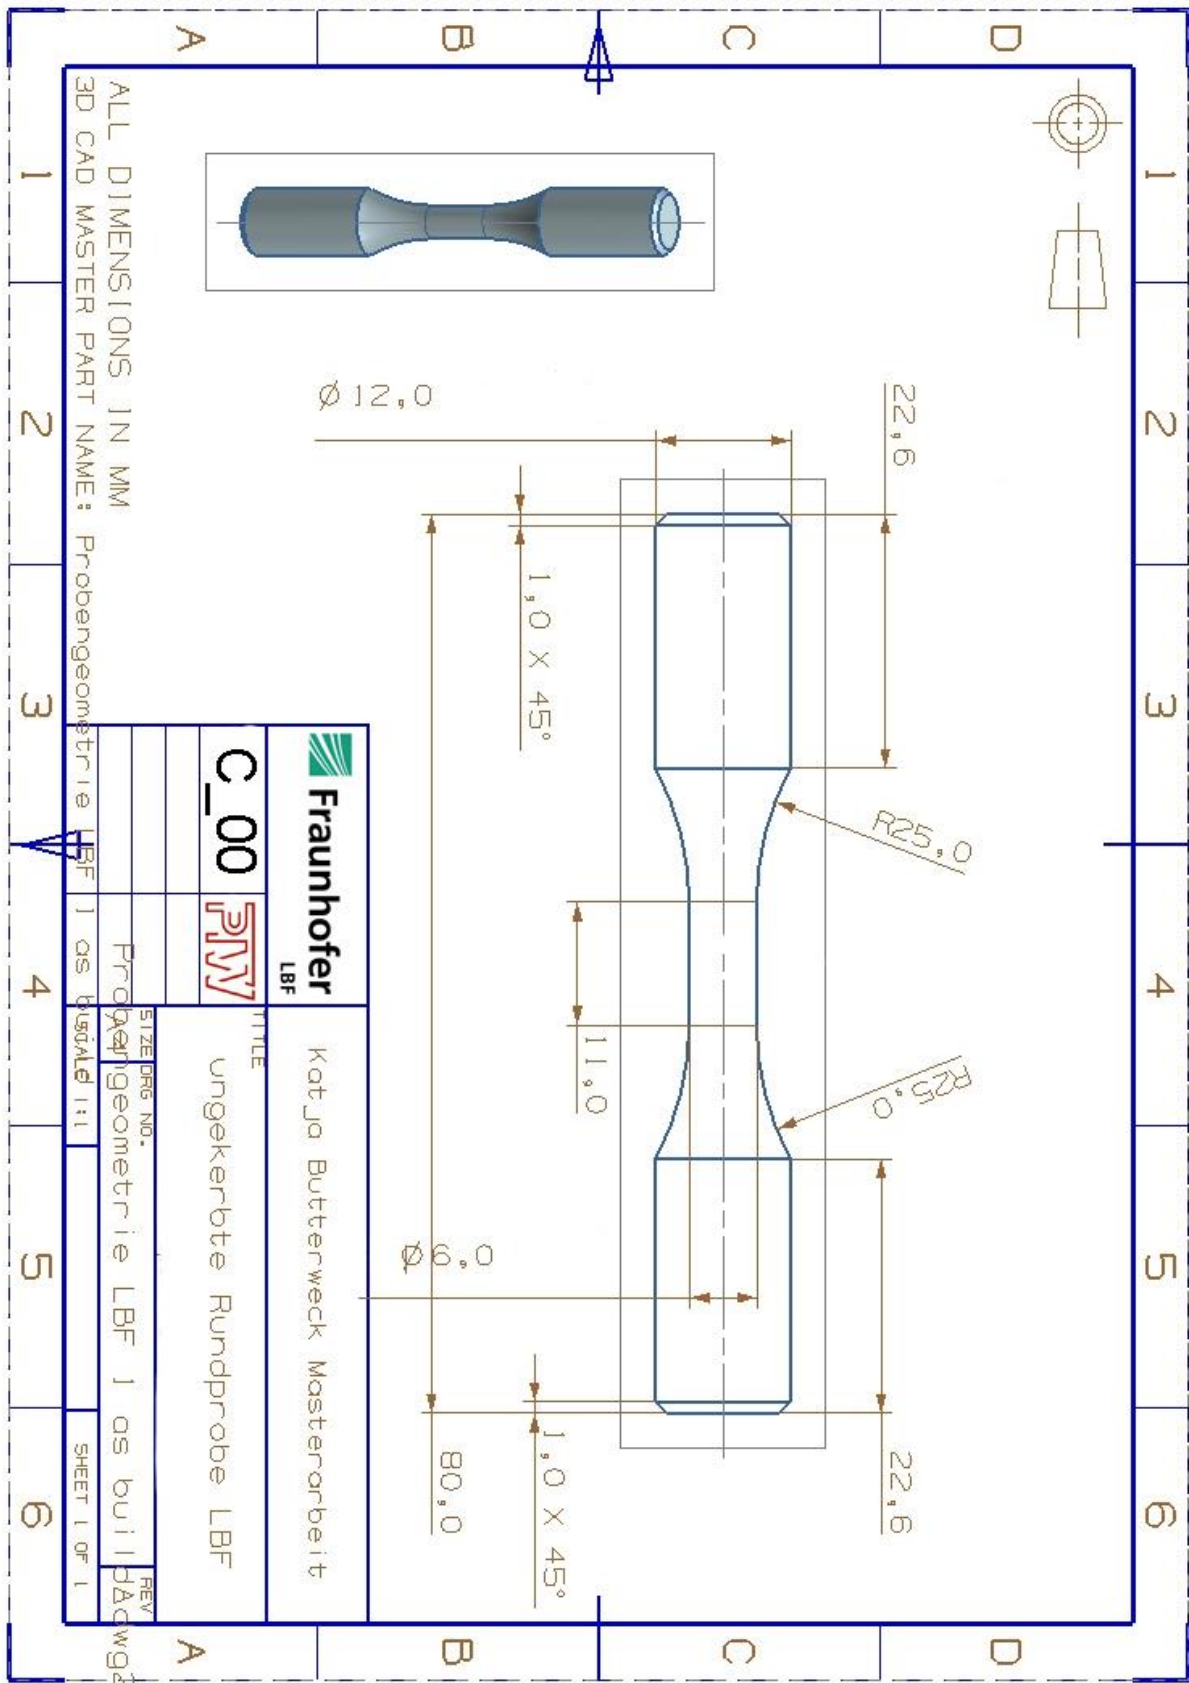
Technische Zeichnung Probengeometrie C_00
